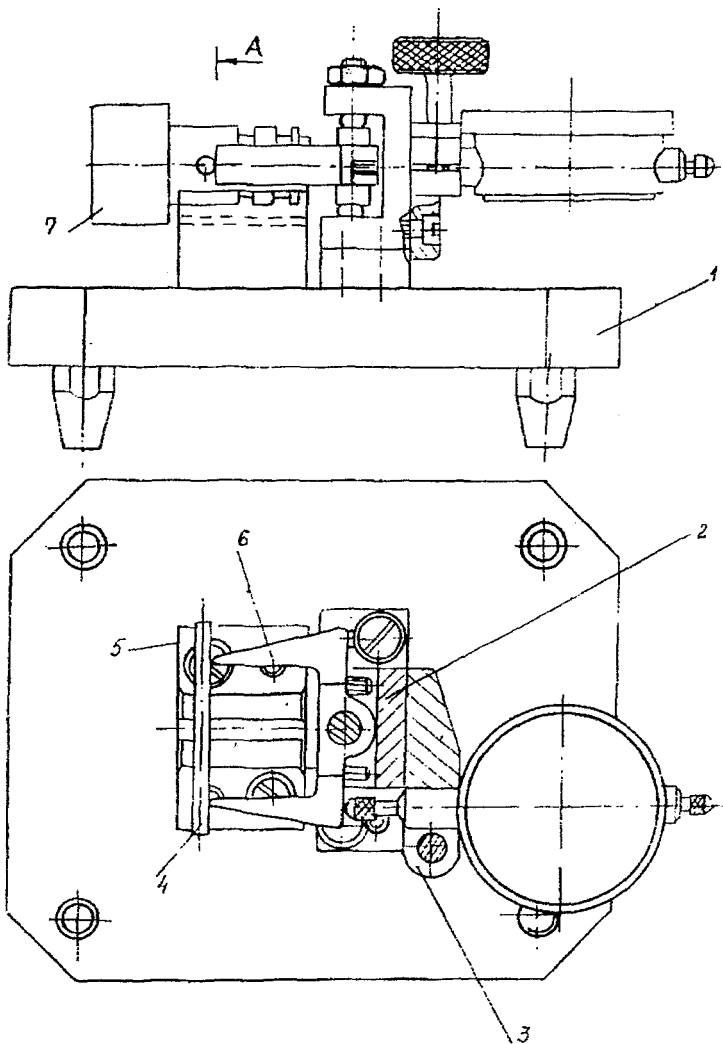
Приспособление для контроля перпендикулярности радиального отверстия к наружному диаметру детали
